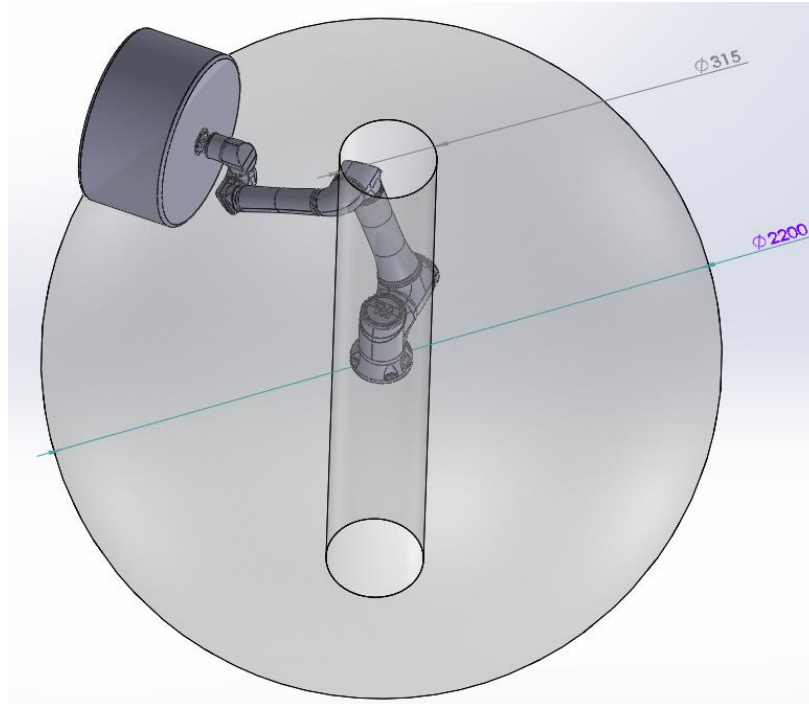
Krajní poloha měření s robotem Universal robots UR 16E
